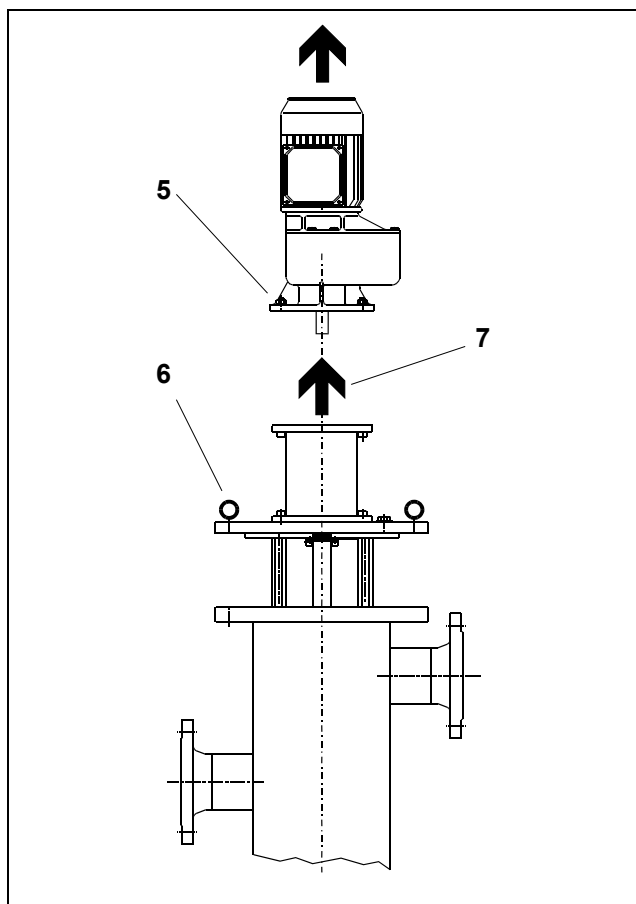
Отвинчивание редукторного электродвигателя и крышки
